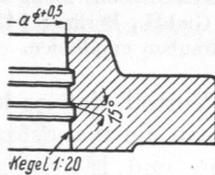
Kegelige Flanschbohrung an Walzflanschen.
